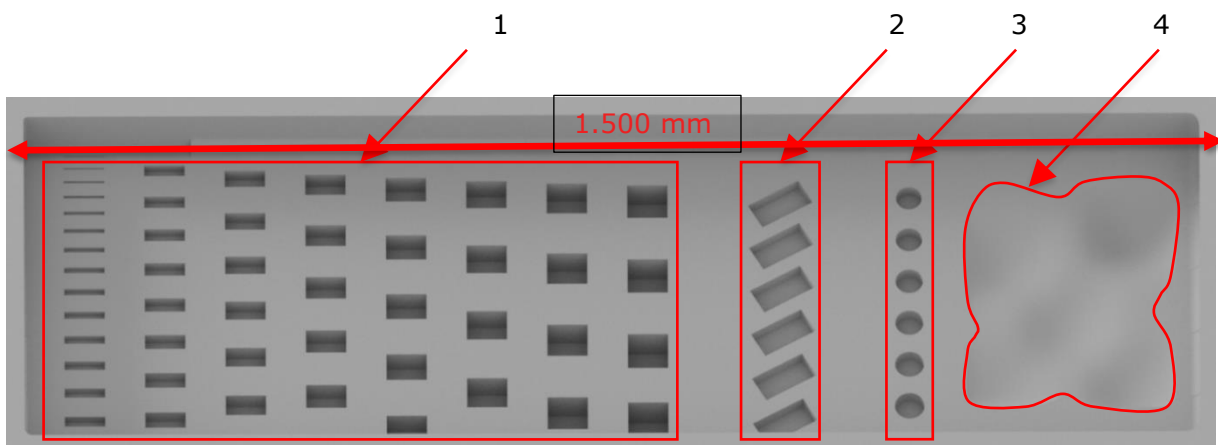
CAD-Modell der Testgeometrie für das Stiftbettwerkzeug
